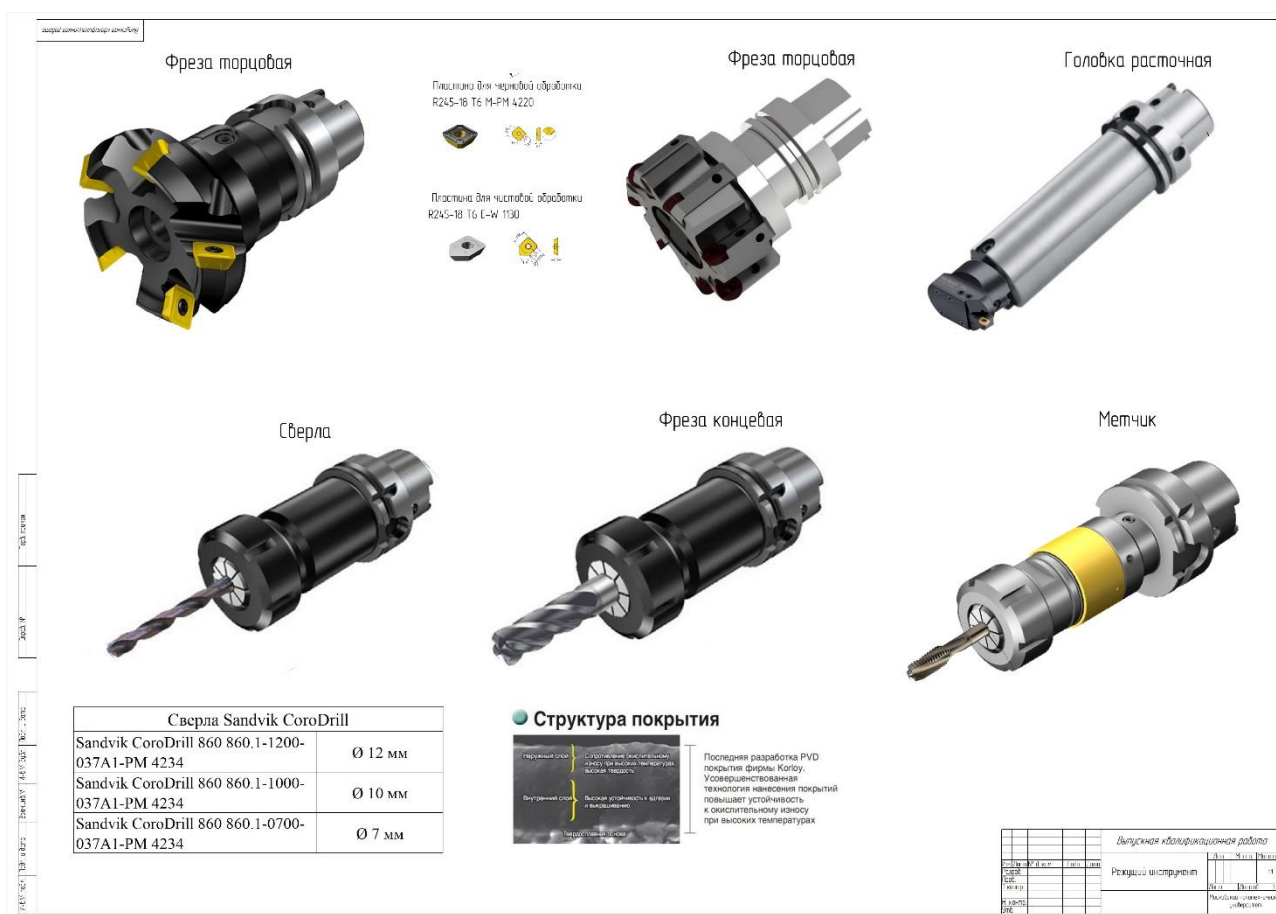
Лист режущего инструмента (выбор инструмента)
